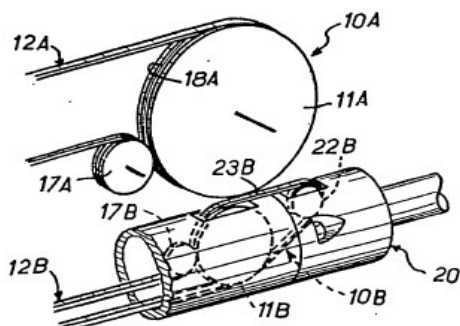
une vue partielle en perspective de la machine soudeuse.
